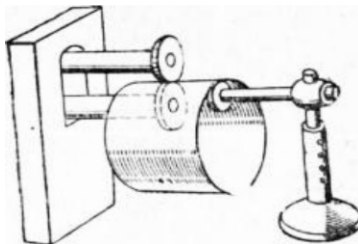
Поддерживающее приспособление для роликовой сварки кольцевых швов обечаек
